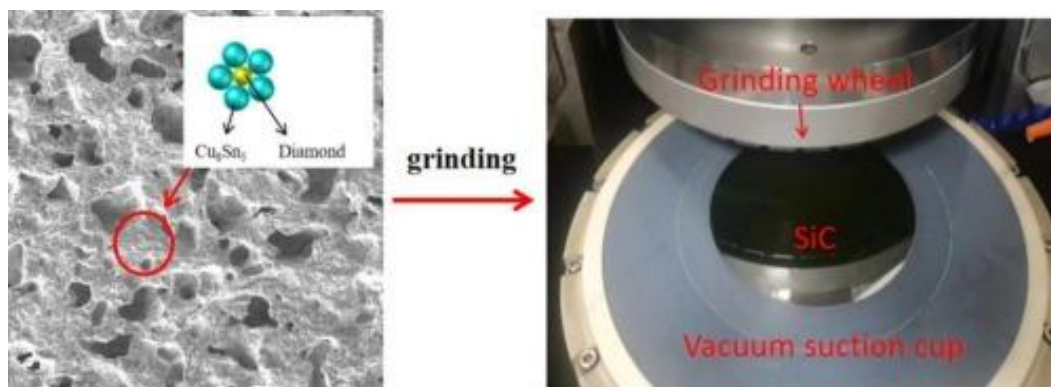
Структура ріжучої поверхні круга з інтерметалічною сполукою Cu_6Sn_5 для якісного шліфування пластин SiC [5].
